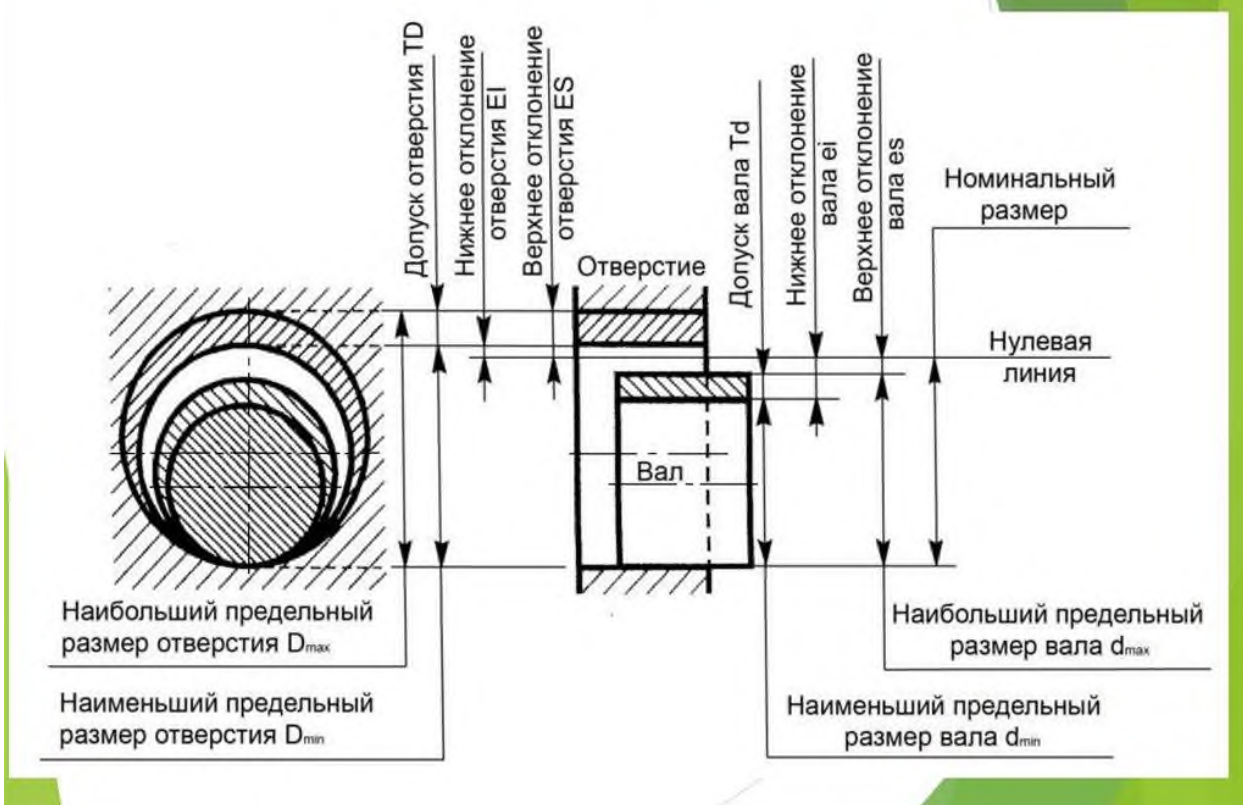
Предельные размеры, отклонения и допуски размера и вала
